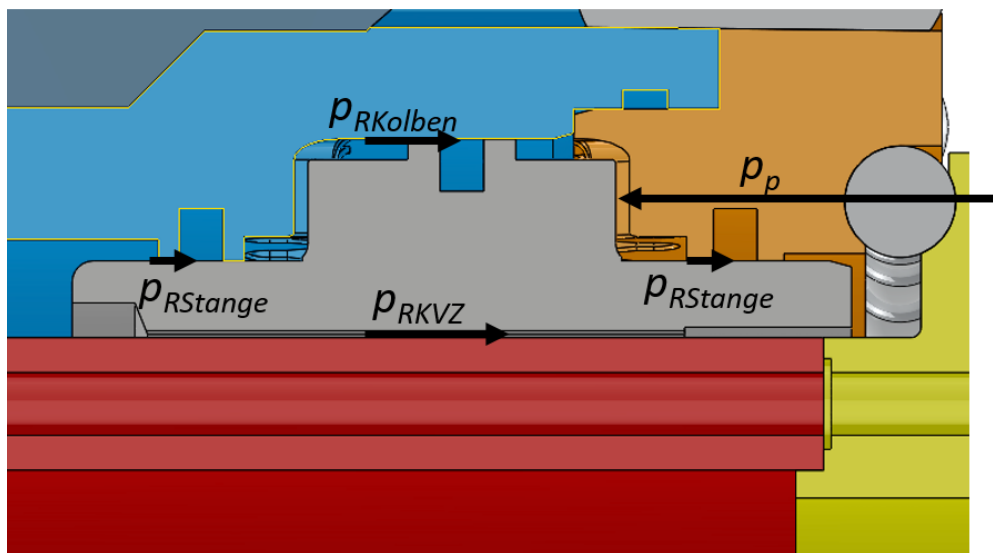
Axiale Reibdrücke an einem Kolben, Quelle: Schwing GmbH
